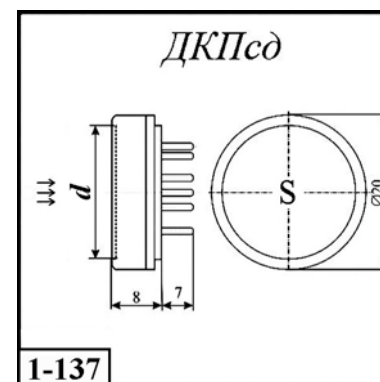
Внешний вид и габаритные размеры детекторов типа ДКПсд.
